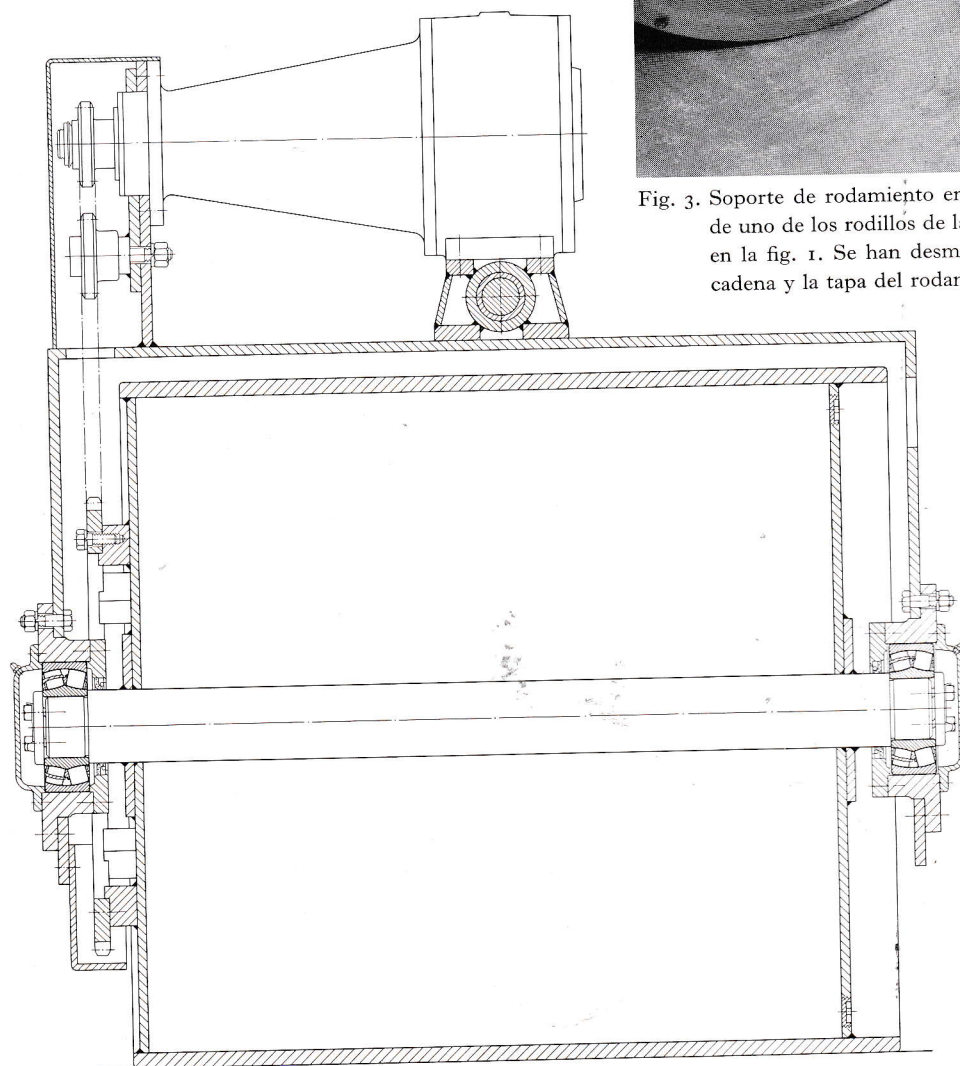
Disposición de rodamientos para el rodillo de la apisonadora representada en la fig. 1
